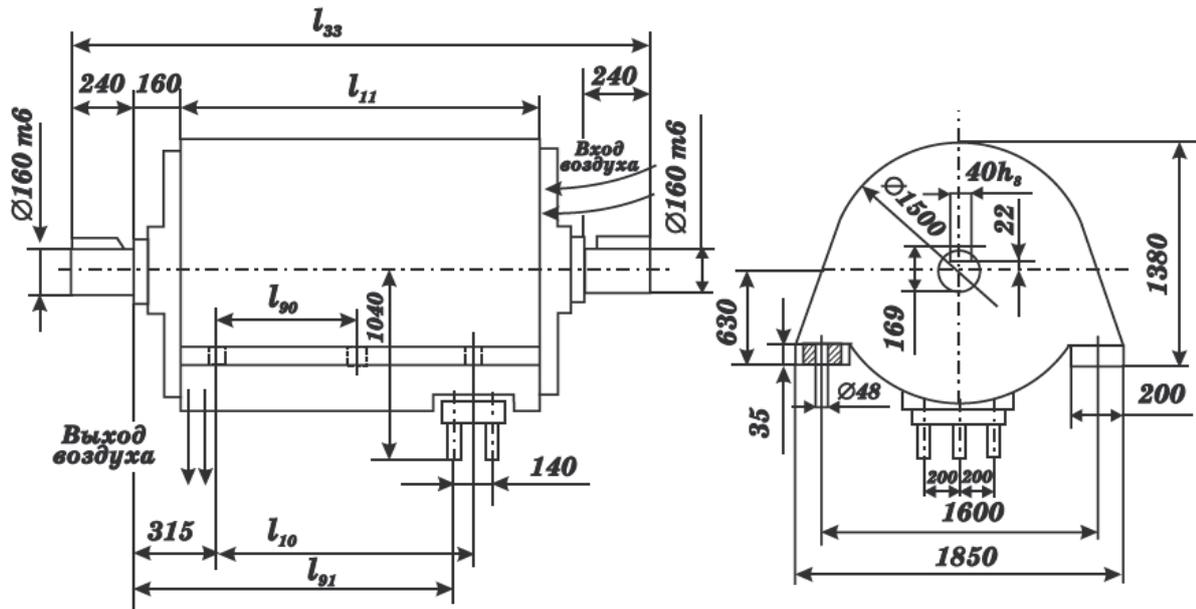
Габаритные, установочные размеры двигателей СДЭ2 16-го габарита напряжением 10 кВ
